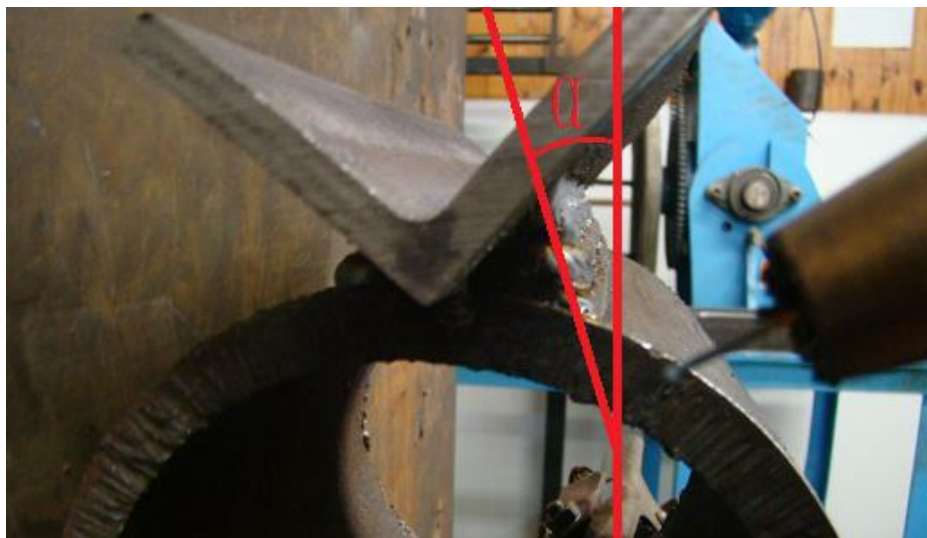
Angulação da superfície dos cordões causada pelo escorrimento na posição de soldagem horizontal
